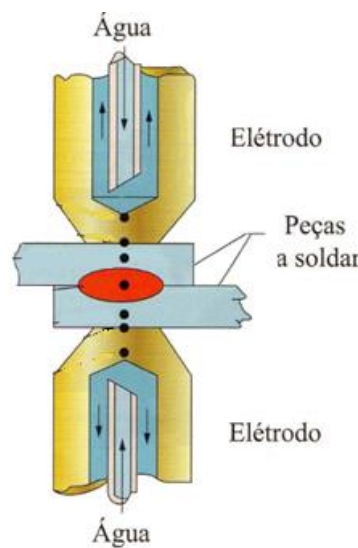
Soldadura por resistência por pontos [35]
